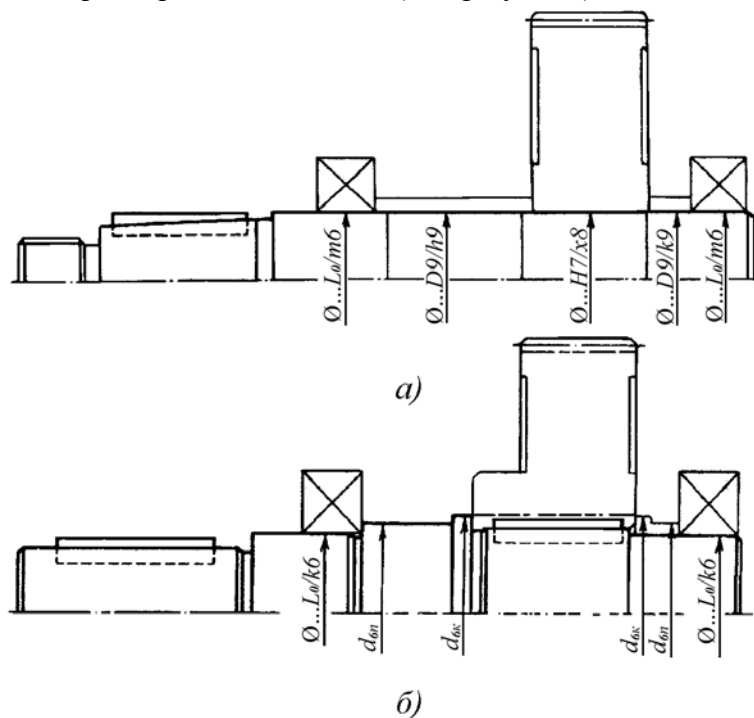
Конструкция вала при различной серийности его изготовления:
